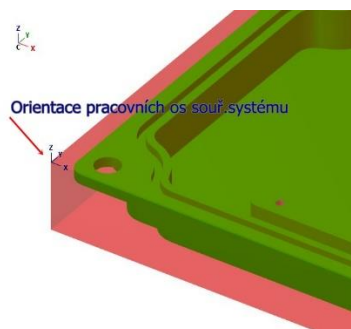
Příklad umístění nulového bodu obrobku u soustružení
